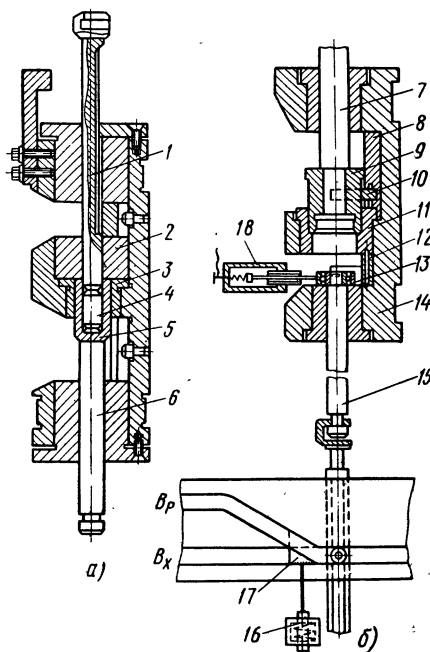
Устройство подвесных пневматических приспособлений для запрессовки деталей:
